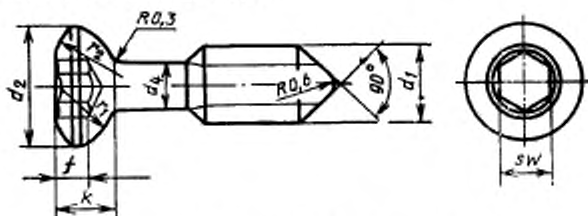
Шуруп с глубокой резьбой (НВ)
